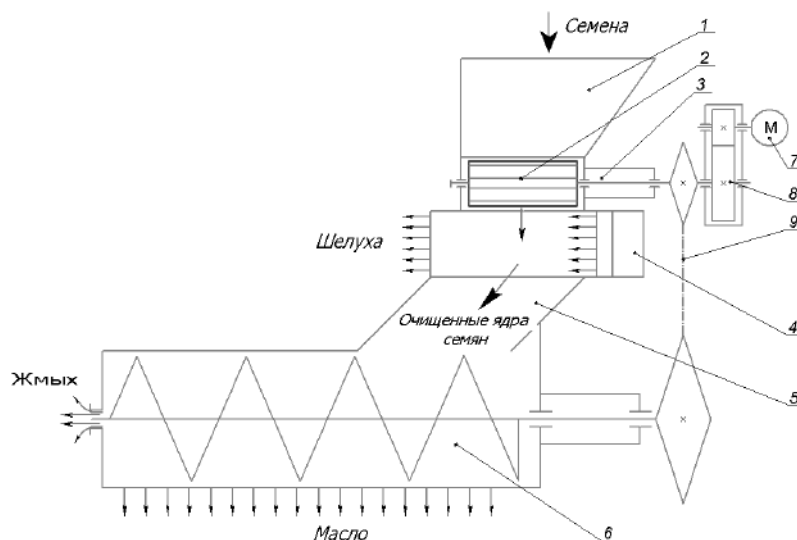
Принципиальная схема шелушитель-пресса для отделения масла: 1 – бункер; 2 – шелушитель; 3 – вальцовый механизм; 4 – вентилятор-сепаратор; 5 – лоток; 6 – шнековый пресс; 7 – электродвигатель; 8 – редуктор; 9 – цепная передача.
